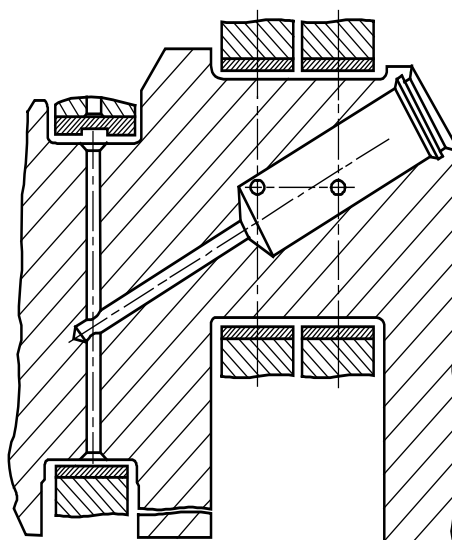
Схема системы смазки коренного и шатунных подшипников
